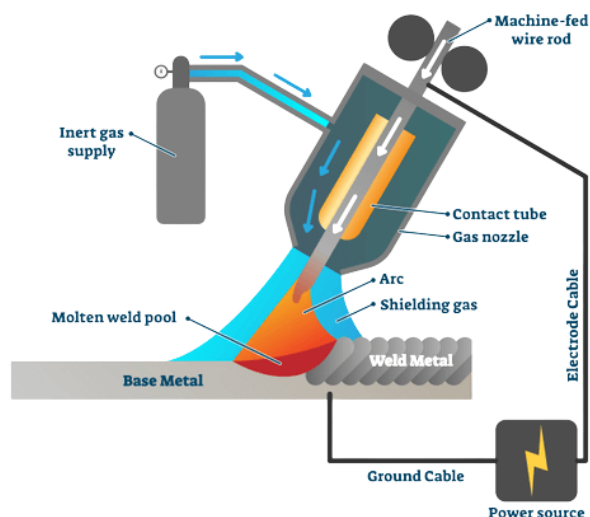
Ilustração do aparato do processo de soldagem MIG (ELECTRONICS..., 2021).
